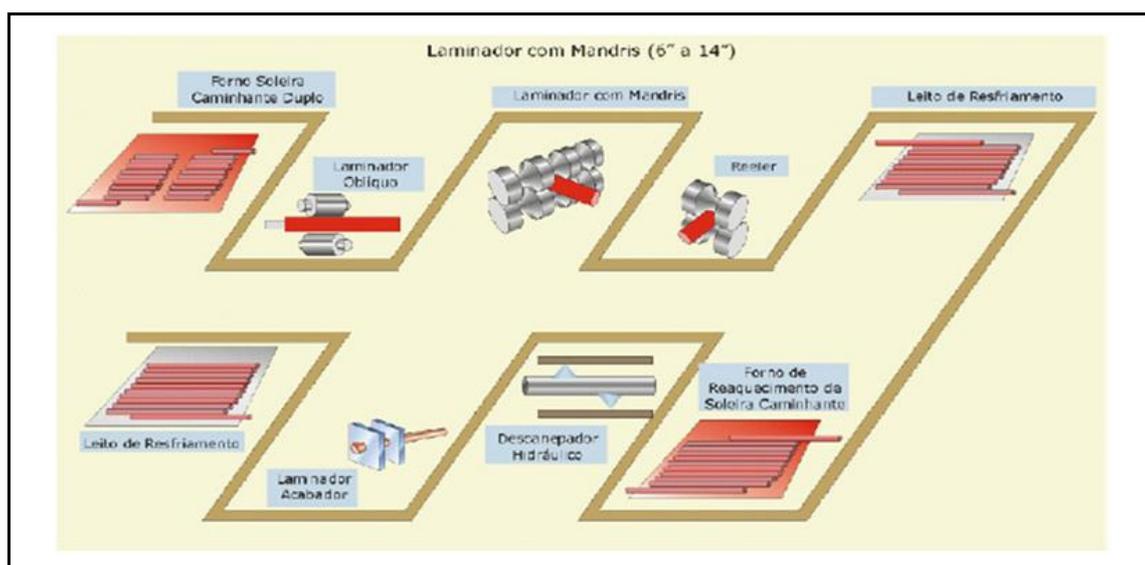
Processo de fabricação na Laminação Automática (LA)
